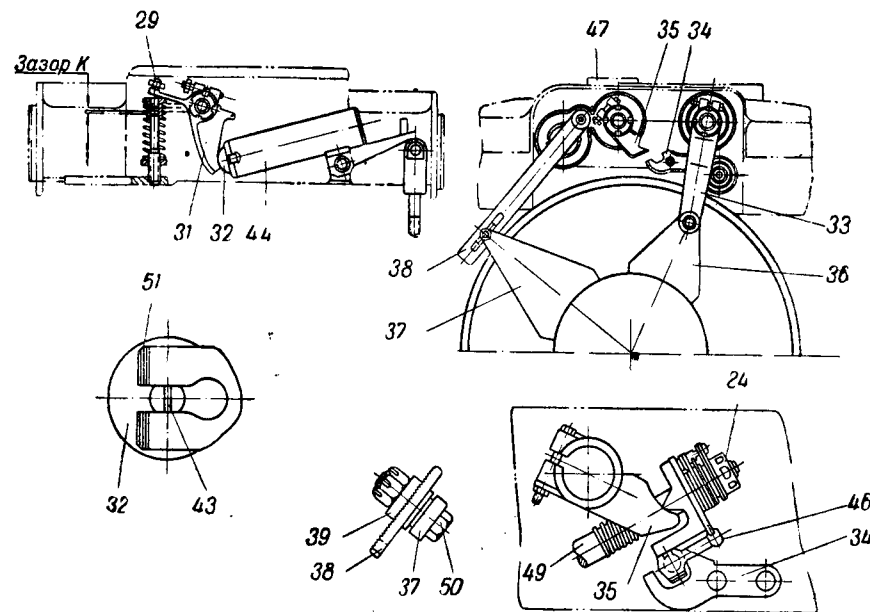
Привод к фрикционным элементам трехскоростного редуктора:
